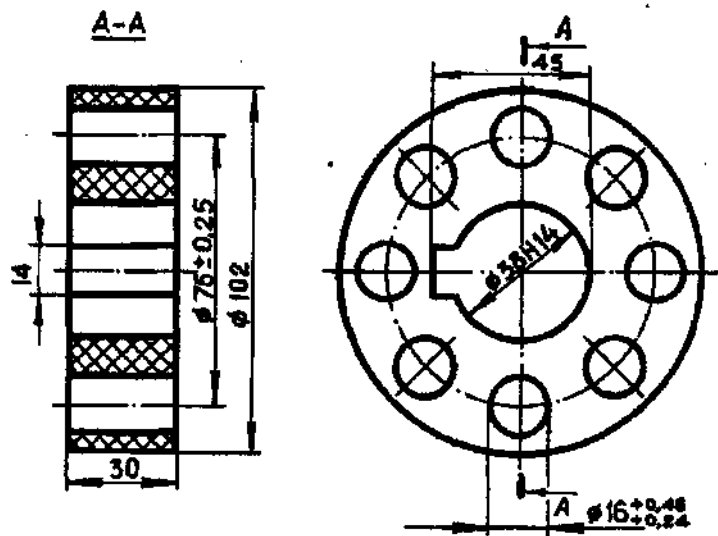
Кольцо. Деталь 6Р13.3.91А
